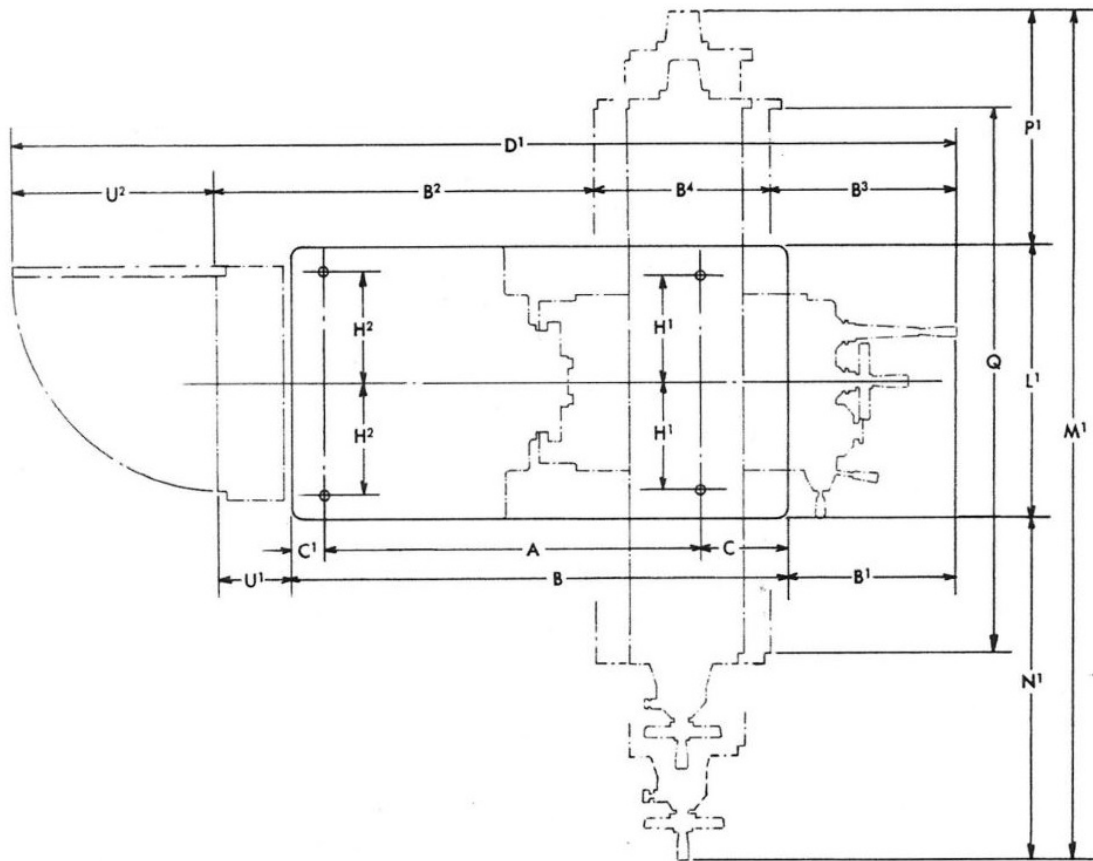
Plano Fresa *Milwaukee* 307 S-12 en Planta
